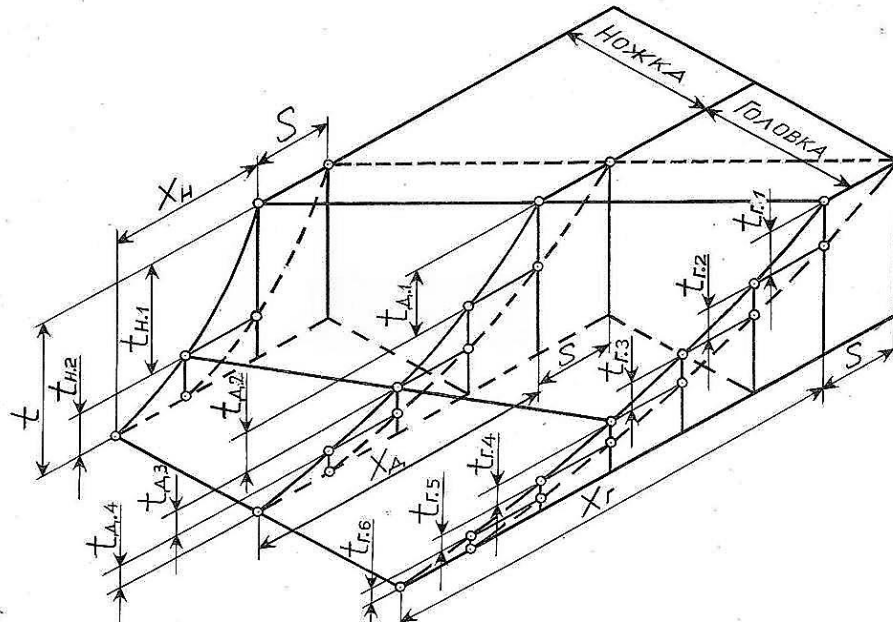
Увеличение длины пятна контакта зуба шестерни с шлифовальным кругом при движении последнего в направлении вершины зуба
